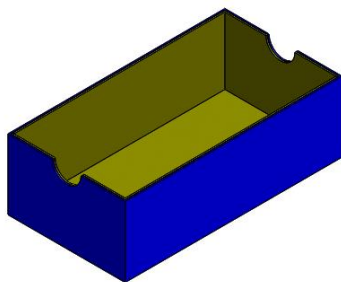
Ensamblaje de la carcasa metálica y el primer aislante
